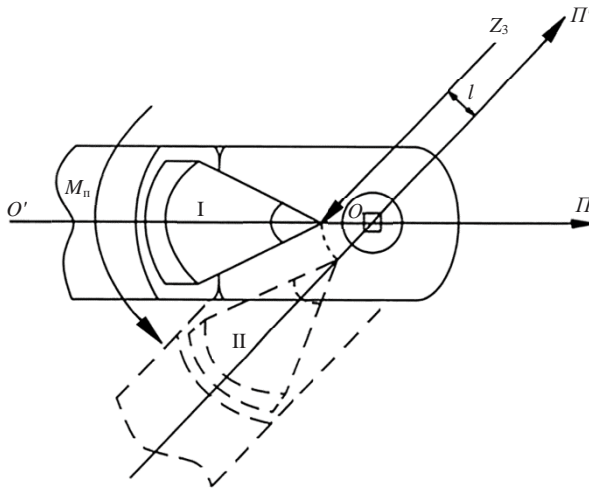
Схема автоматической самоустановки резца при работе горного комбайна
